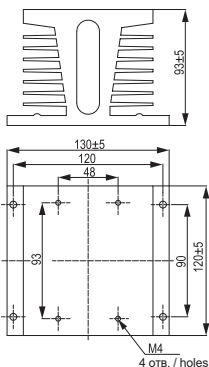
Габаритные и установочные размеры радиатора / Figure 11 - Overall and mounting dimensions of the heat sink / 11 сурет – Радиатордың габариттік және орнату өлшемдері RSS-1-100
